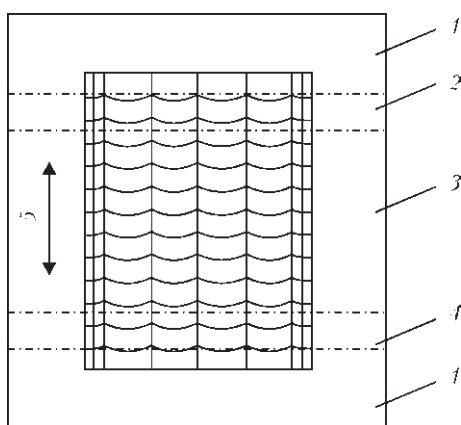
Порядок вырезки образцов из наплавленной пластины (контрольный образец): 1 — неконтролируемая область ≥ 25 мм; 2 — область для вырезки образца для испытаний на поперечный изгиб; 3 — область для вырезки образца для исследований макроструктуры, образца для химического анализа и определения содержания дельта-феррита; образца для исследований микроструктуры с замером твердости; область для вырезки образцов для повторных исследований; 4 — область для вырезки образца для испытаний на поперечный изгиб; 5 — направление наплавки
